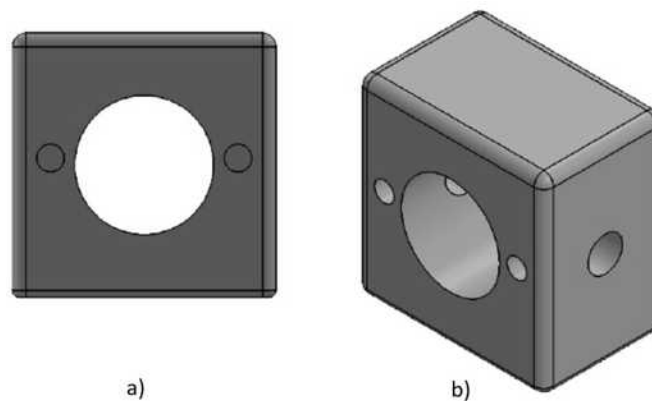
7.- Rodamiento. a) vista frontal, b) vista isométrica.
